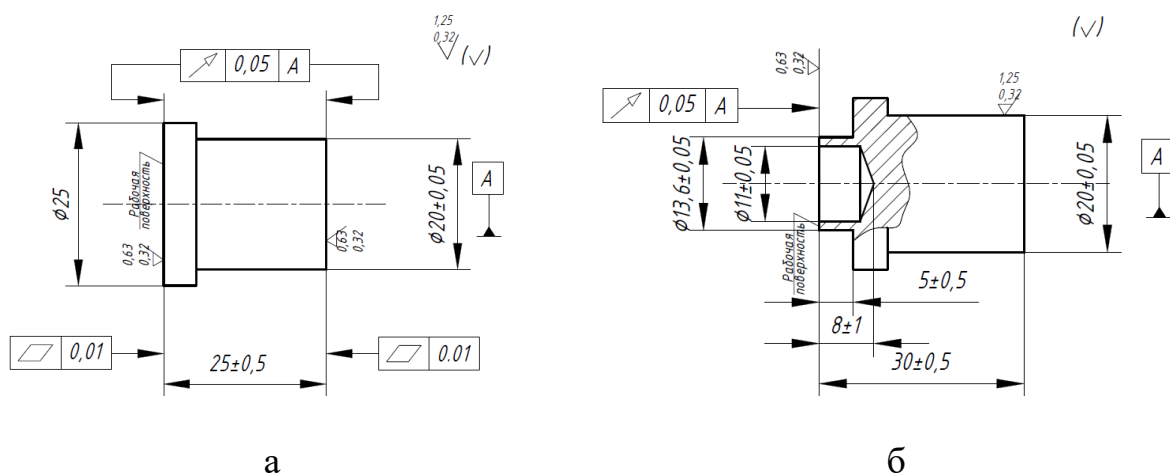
Чертежи образцов для испытаний [85]:
